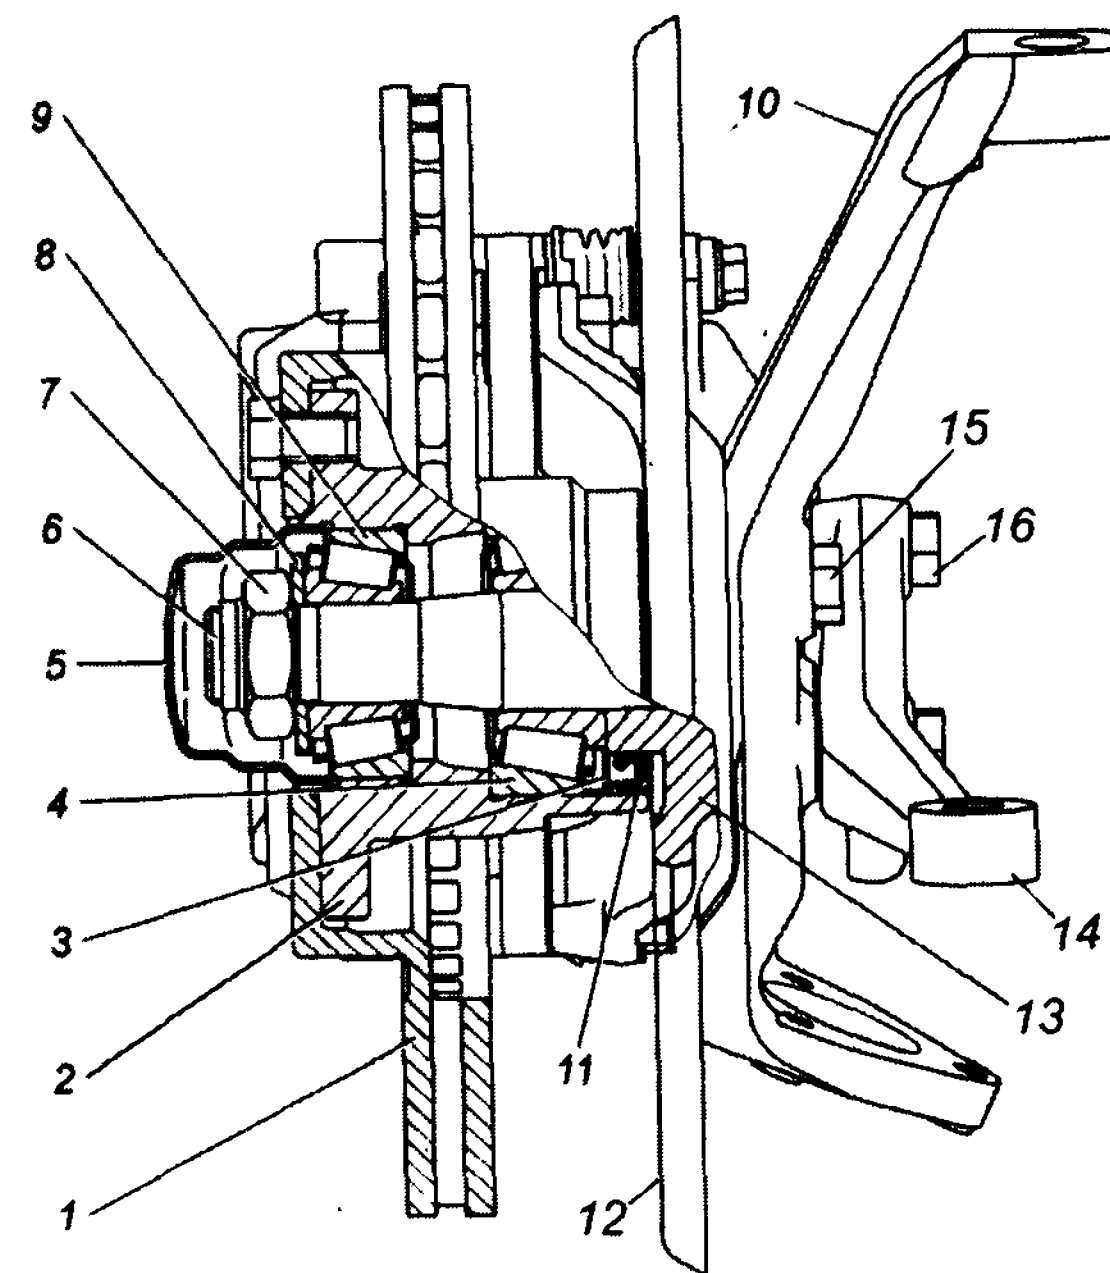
Ступичный узел: 1 – тормозной диск; 2 – ступица; 3 – упорная шайба; 4, 9 – подшипники конические; 5 – колпак ступицы; 6 – цапфа; 7 – гайка ступицы; 8 – шайба; 10 – стойка; 11 – манжета; 12 – тормозной щит; 13 – кронштейн; 14 – рычаг поворотный; 15, 16 – болты
